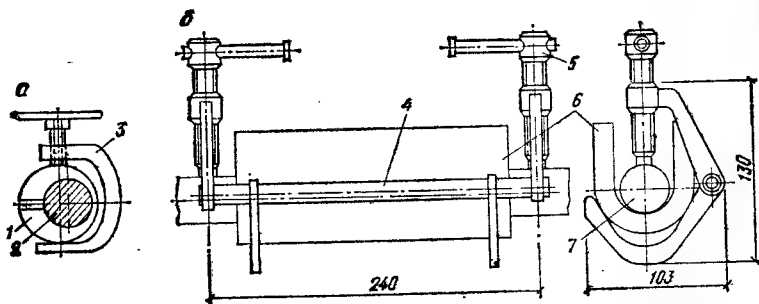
Приспособление для крепления медной формы и подкладки
